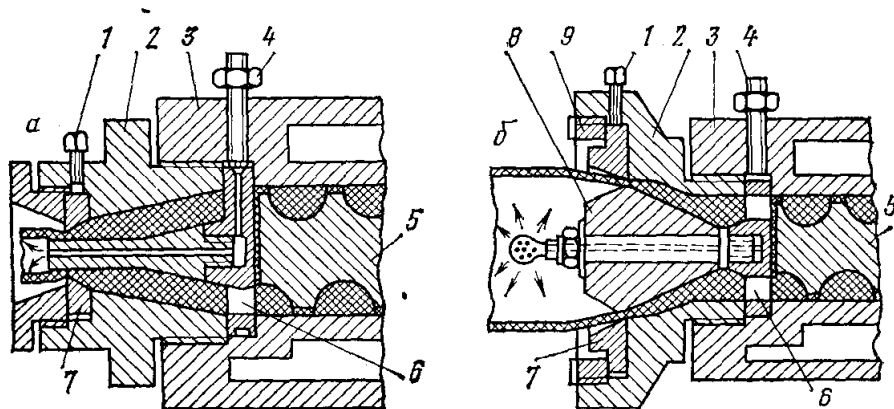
Голівка для виготовлення труби (а) і заготівки автомобільних камер (б) :
